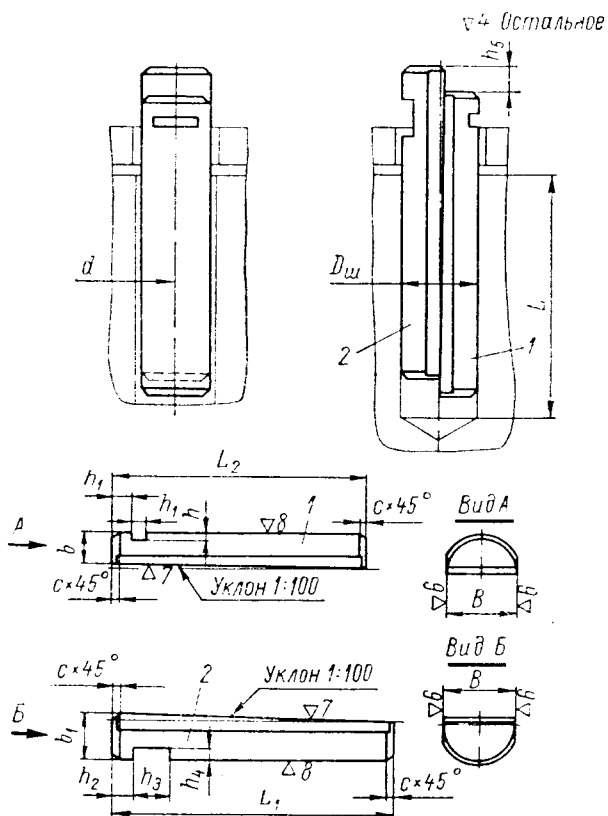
Шпонка разрезная цилиндрическая:
